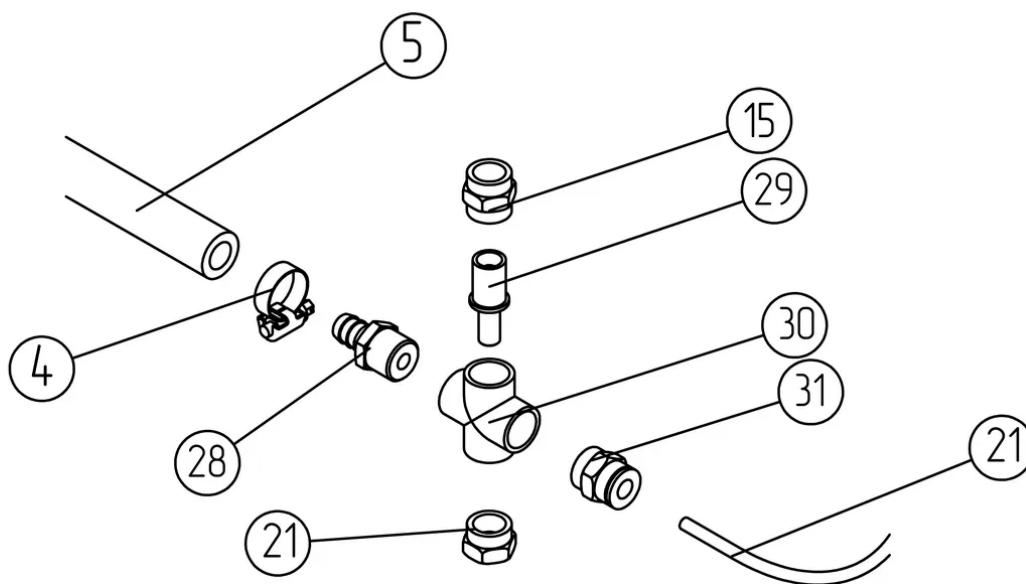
Схема сборки узла подачи песка (обозначения деталей см. согласно Рисунку 1)
